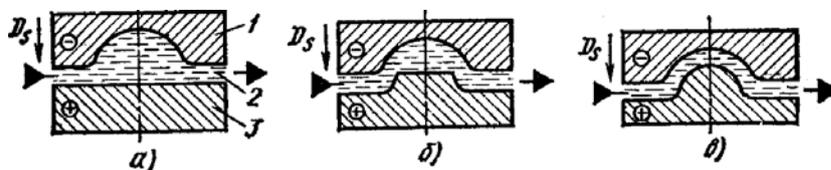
Схема последовательного (а,б,в) формообразования поверхности заготовки: 1 – электрод-инструмент; 2 – струя электролита; 3 – электрод-заготовка
